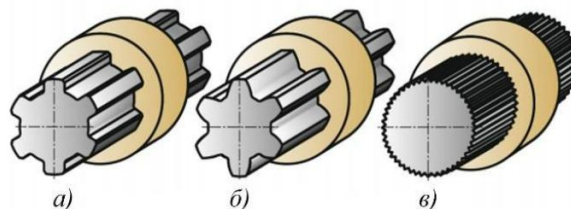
Типы шлицевых соединений: а) – с прямобочными шлицами; б) с эвольвентными шлицами; в) с треугольными шлицами
